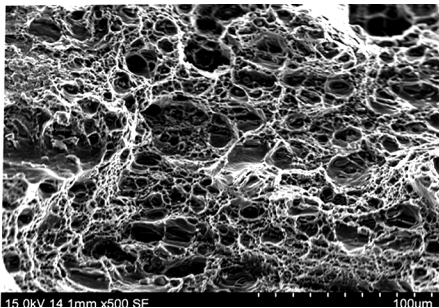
焊缝匙孔修补位置接头断口微观形貌
